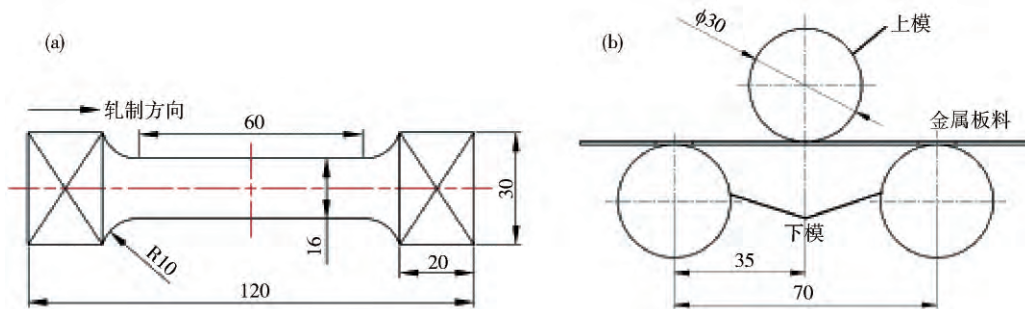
试件和弯曲模具尺寸. (a) 试件尺寸; (b) 弯曲模具尺寸 (单位: mm)
